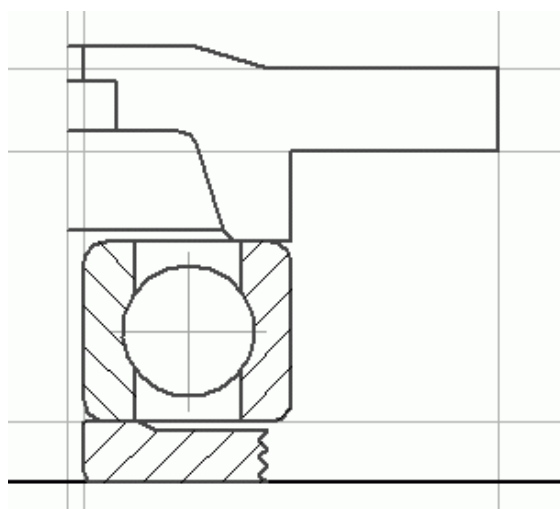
Вычерчивание сквозной крышки подшипника ведомого вала
